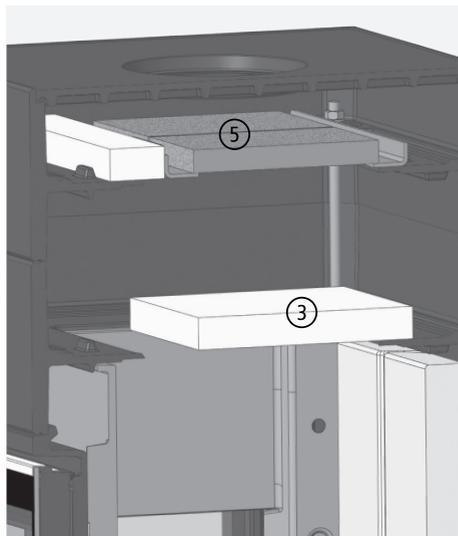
Position des plaques du catalyseur du CORNA ES tec, vue en coupe
